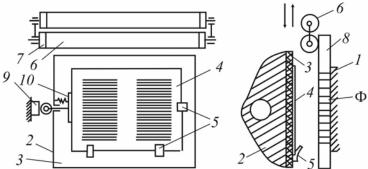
Схема тигельного печатного аппарата: 1 — талер; 2 — тигель; 3 — декель; 4 — лист; 5 — упоры; 6 — красконакатные валики; 7 — опорные кольца; 8 — регулировочные планки; 9 — горка; 10 — толкатель; Φ — форма
